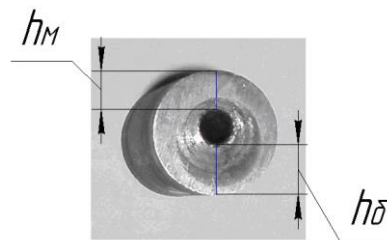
Разметка положений наибольшей и наименьшей толщины стенок на торце детали со стороны выхода инструмента
